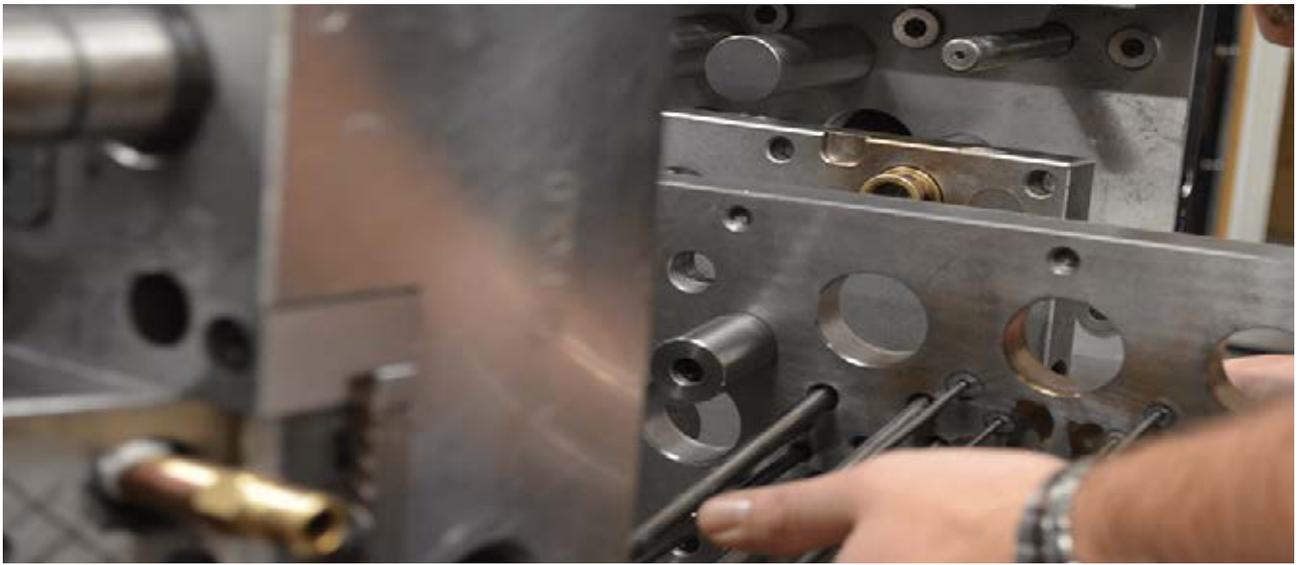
：導入 CAE 模流分析 Moldex3D，配搭無縫整合模具 CAD、製造 CAM，與生產現場累積之相關參數，形成大量數據庫加以分類歸納，以供設計、製造、生產人員參考
